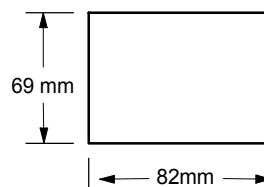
Размеры отверстия для установки устройства TD 100C
